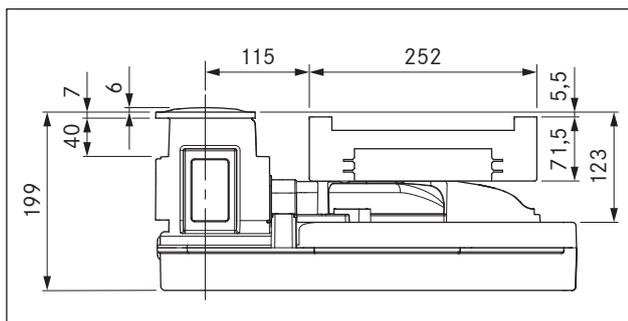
Dimensions PKAS, PKASAB vue de face
